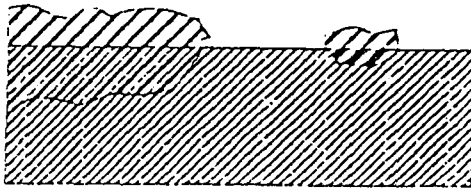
Kaynak bölgesinde taneler arası korozyon
